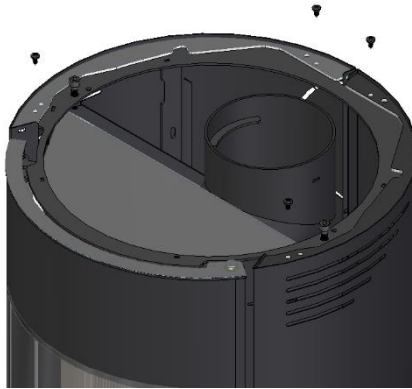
Démontez les couvercles latéraux de l'équipement
